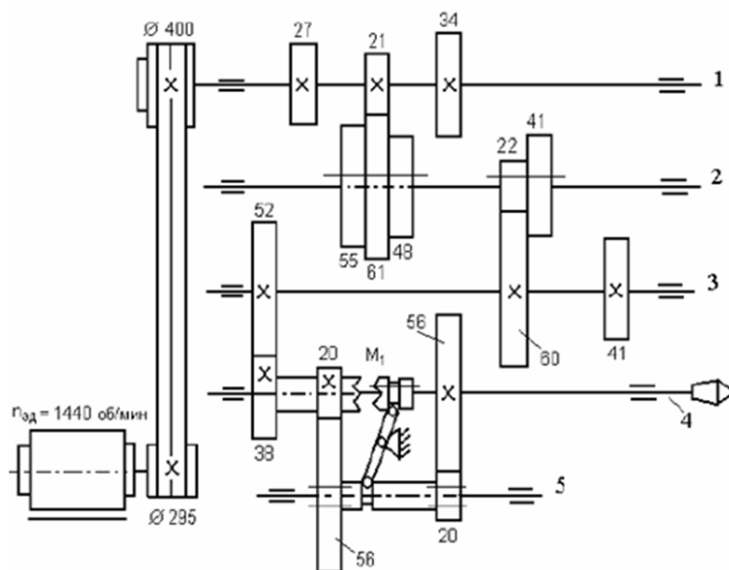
Двенадцатиступенчатая коробка передач станка
